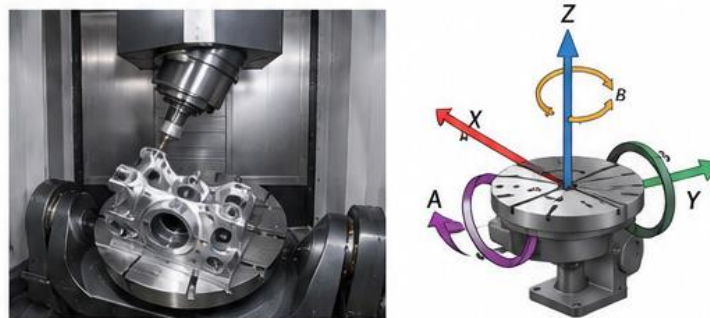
5-осьовий обробний центр з ЧПК[8]
